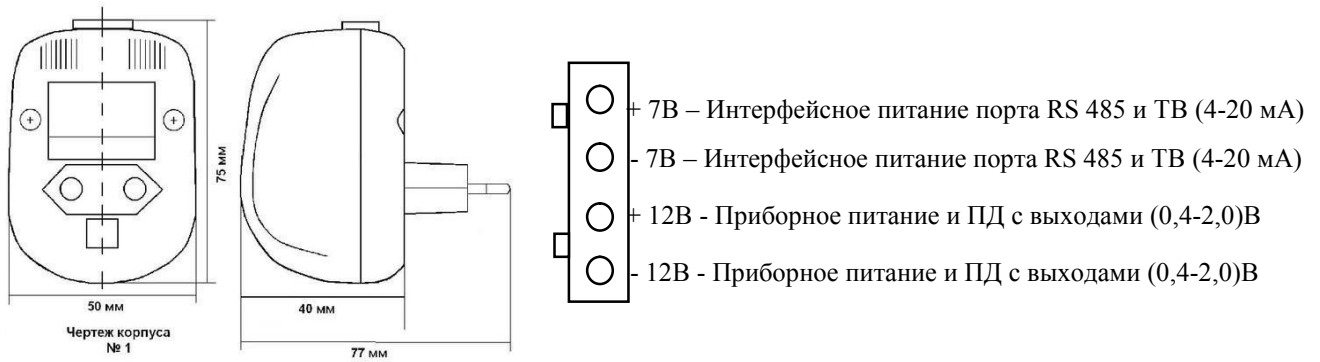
Размеры корпуса источника питания БП-5.
